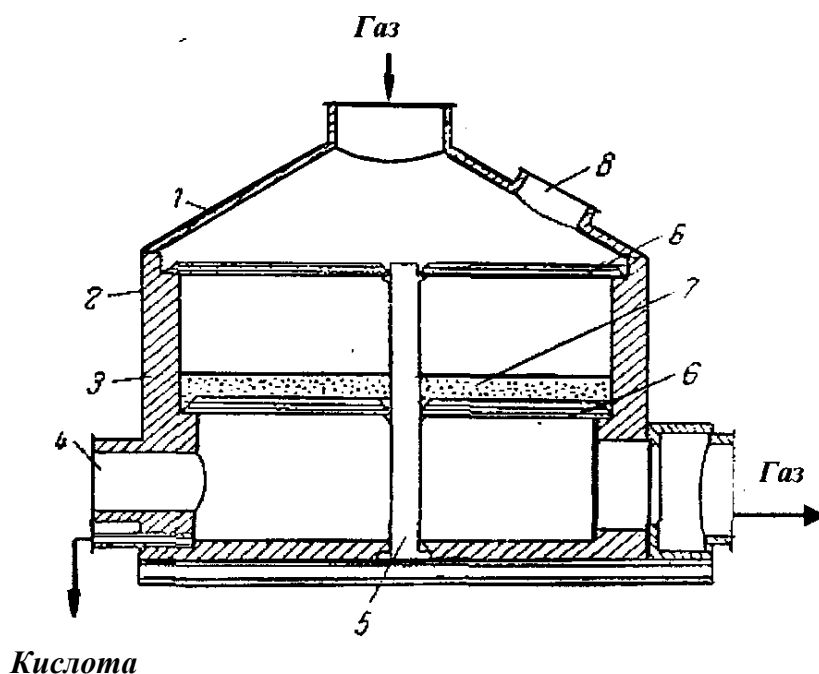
Волокнистый фильтр: 1 – крышка; 2 – корпус; 3 – футеровка; 4 – лаз; 5 – опорная колонка; 6 – распределительные плиты; 7 – фильтрующий слой; 8 – люк для загрузки фильтра (типовой) типа ЦН-15 (конструкции НИОгаз). Диаметр аппарата –  $\varnothing 800$  мм.
